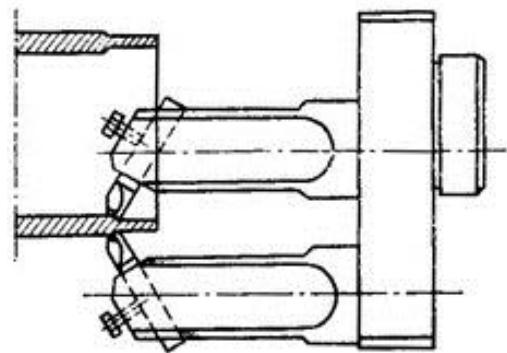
Двухрезцовая державка для одновременной расточки и обточки маслоты
